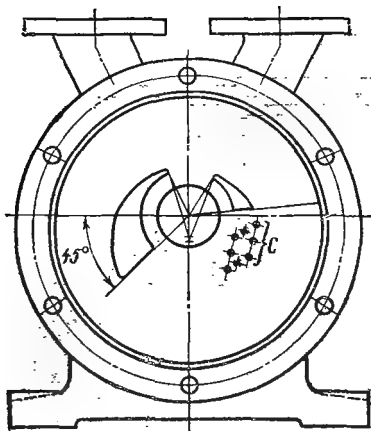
Вид на торцовую крышку со стороны рабочего колеса
